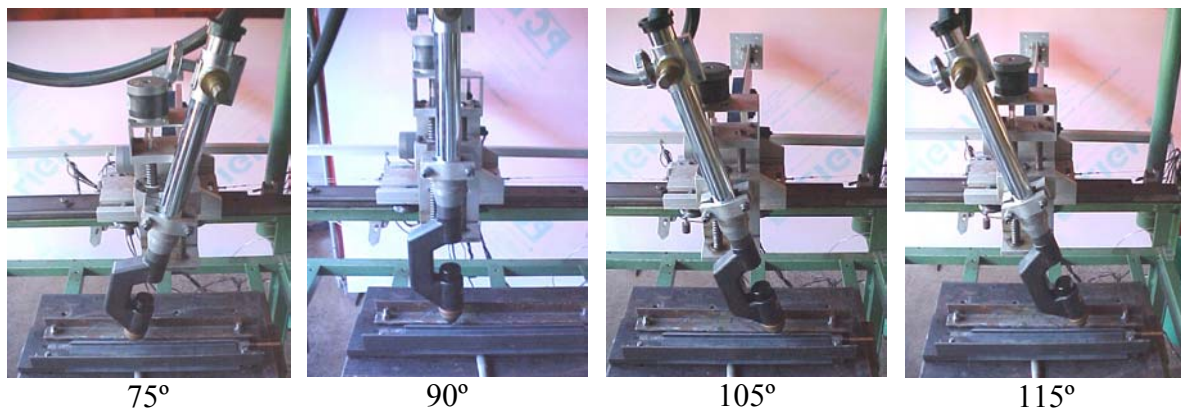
Ângulos de ataque da tocha de soldagem para soldagens da esquerda para direita
